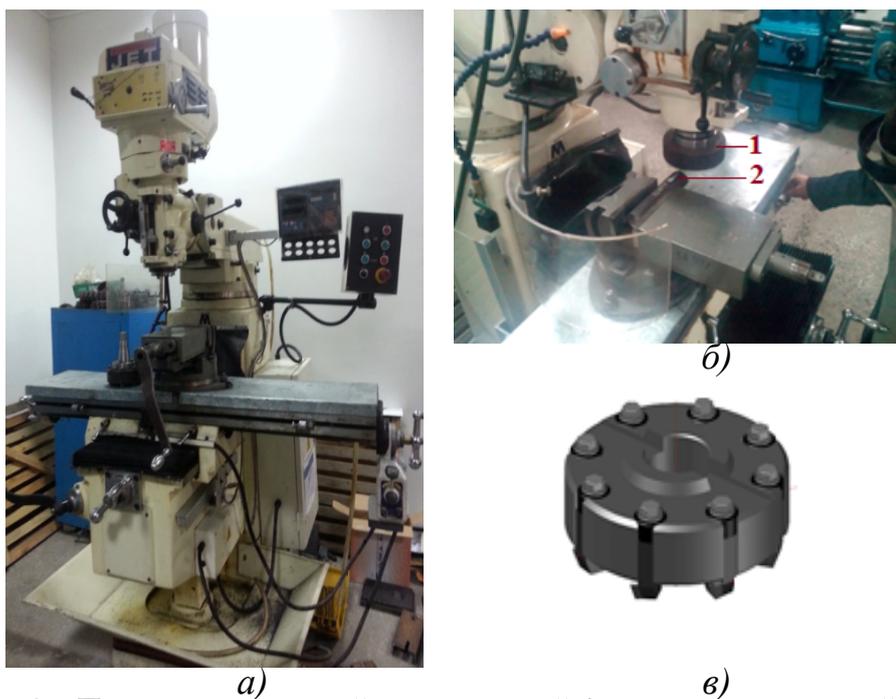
Полуавтоматический вертикальный фрезерно-сверлильный станок, режущий инструмент и процесс обработки
